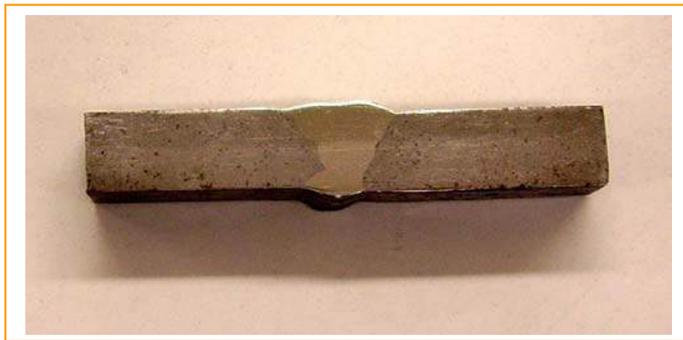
Dos piezas unidas mediante soldadura homogénea.
